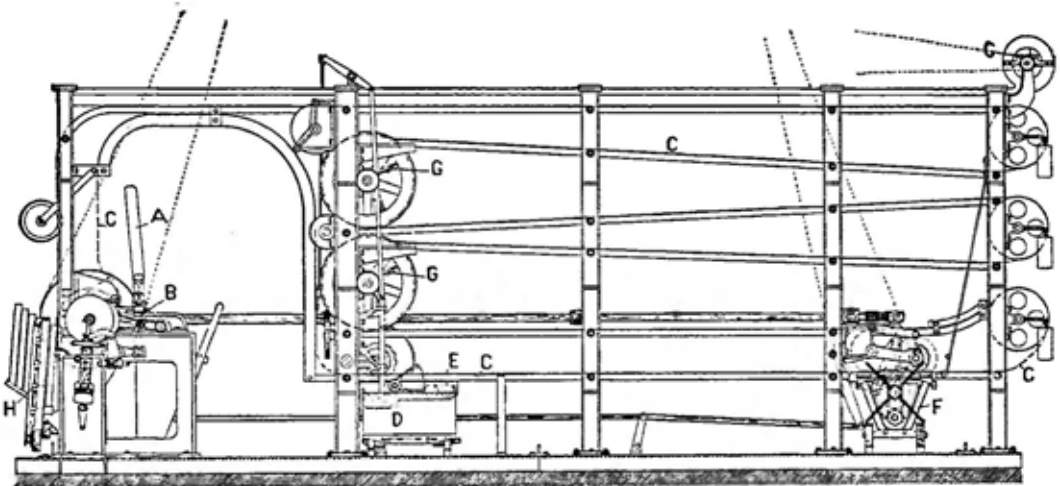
Kompletmaschine „Neue Simplex“ (Seitenansicht) der MASCHINENFABRIK A. ROLLER, Berlin. A Holzdrahtmagazin; B Holzdrahteinstoßapparat; C Holzdrahtkette; D Nachwärmplatte; E Paraffinierapparat; F Tunkapparat; G Ventilator; H Hölzerabfüllapparat.
